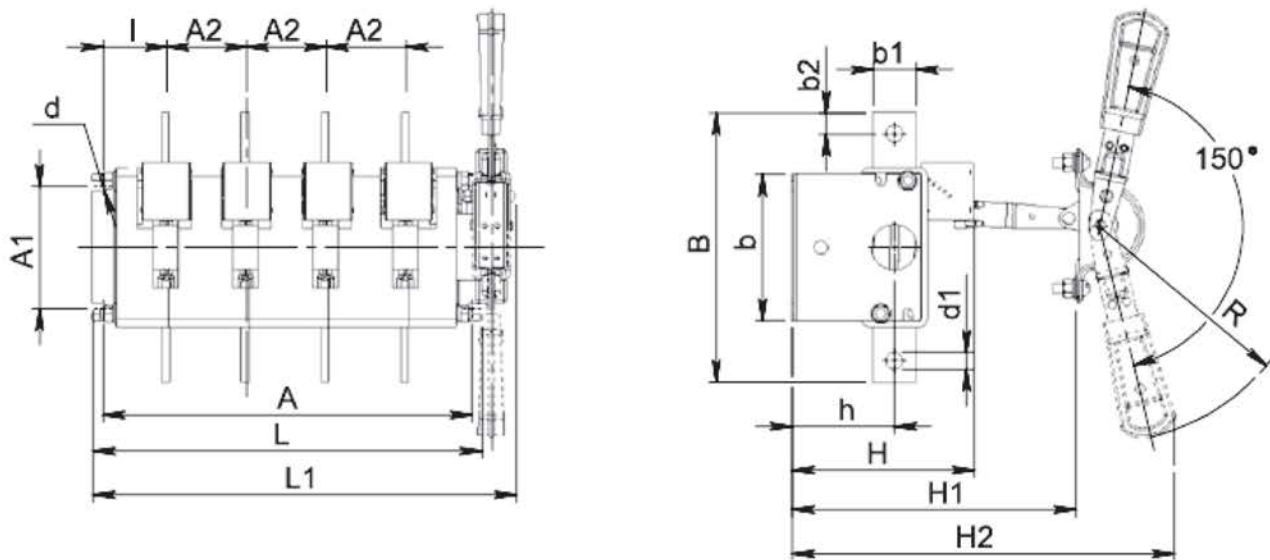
Выключатель-разъединитель четырехполюсный на два направление с боковой рукояткой.
